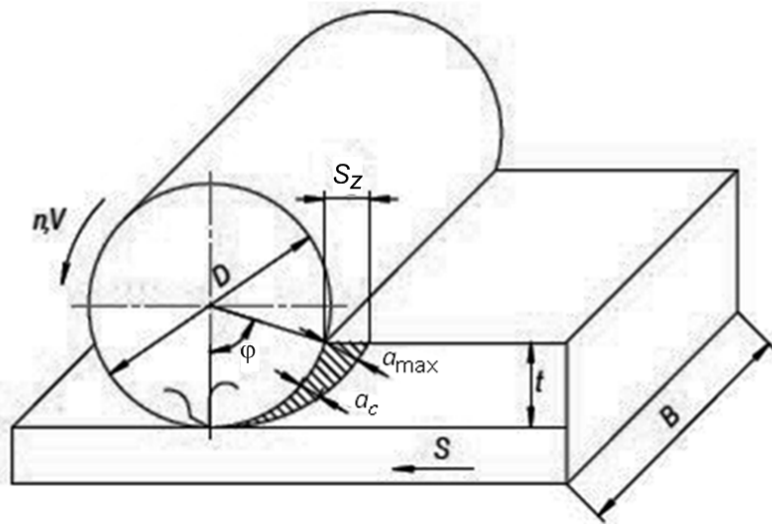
Елементи режиму різання при фрезеруванні
